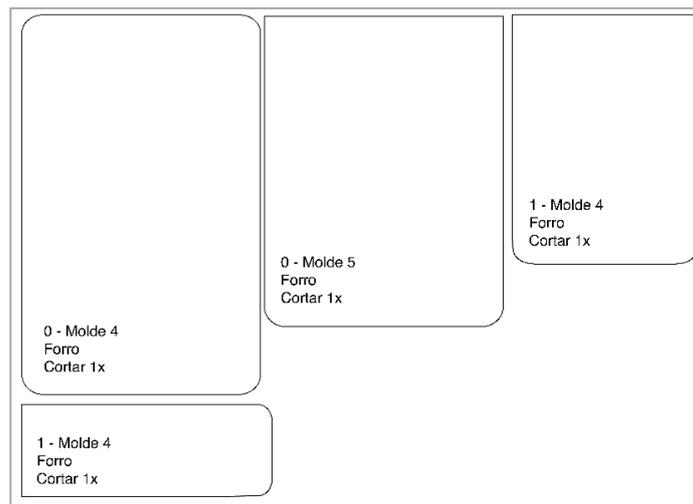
Plano de corte - Feltro (Fonte: Autor)
